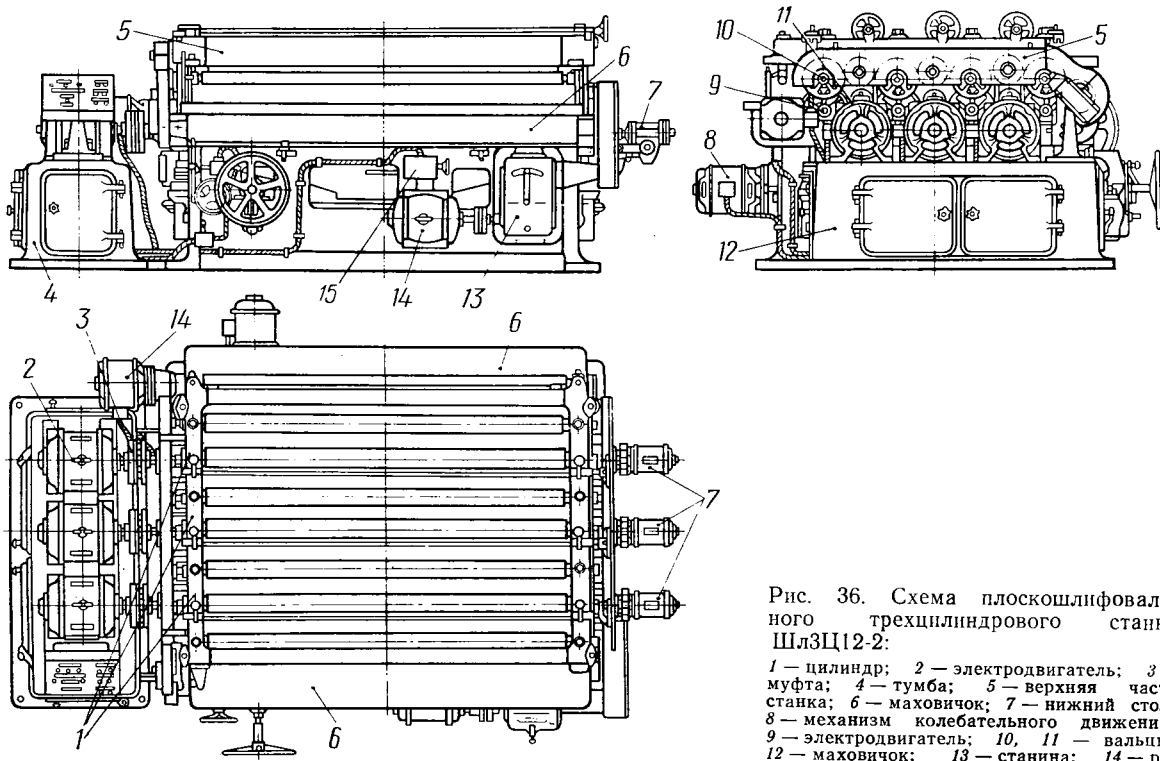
Схема плоскошлифовального трехцилиндрового станка ШлЗЦ12-2:
